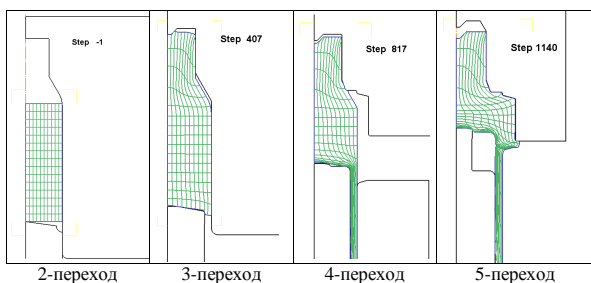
Конфигурация формообразующего инструмента и обрабатываемой заготовки по базовой технологии на момент начала перехода ХОШ
